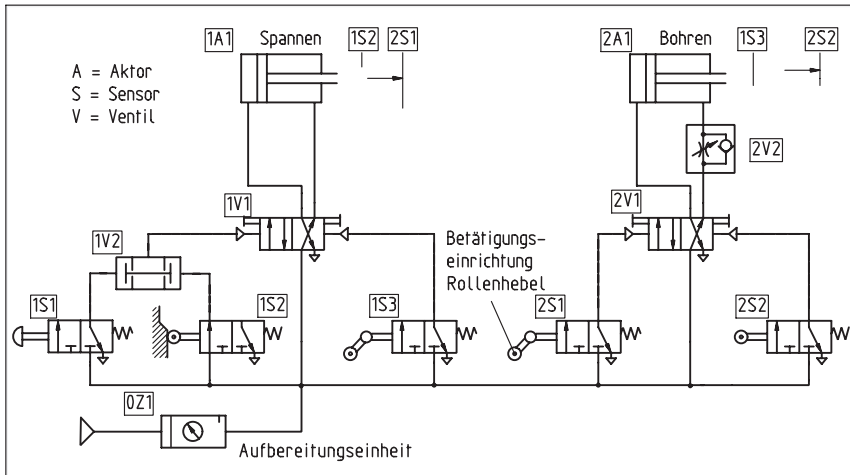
Schaltplan einer Bohreinrichtung
